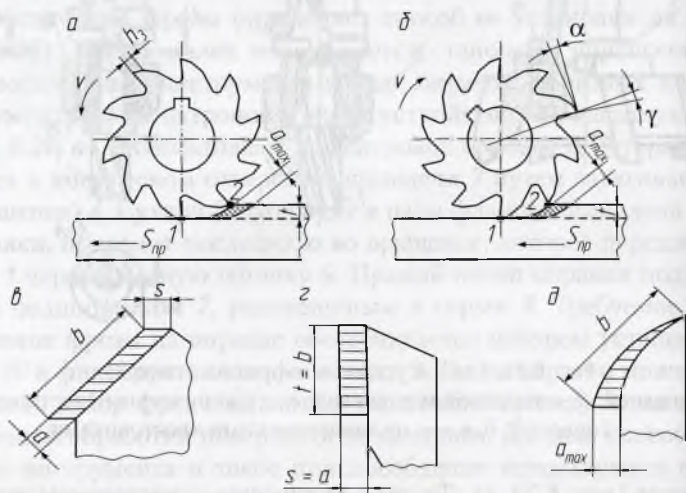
Схемы встречного (а) и попутного (б) фрезерования; форма стружки при точении проходным (в) и проходным упорным (з) резцами и при фрезеровании (д)
